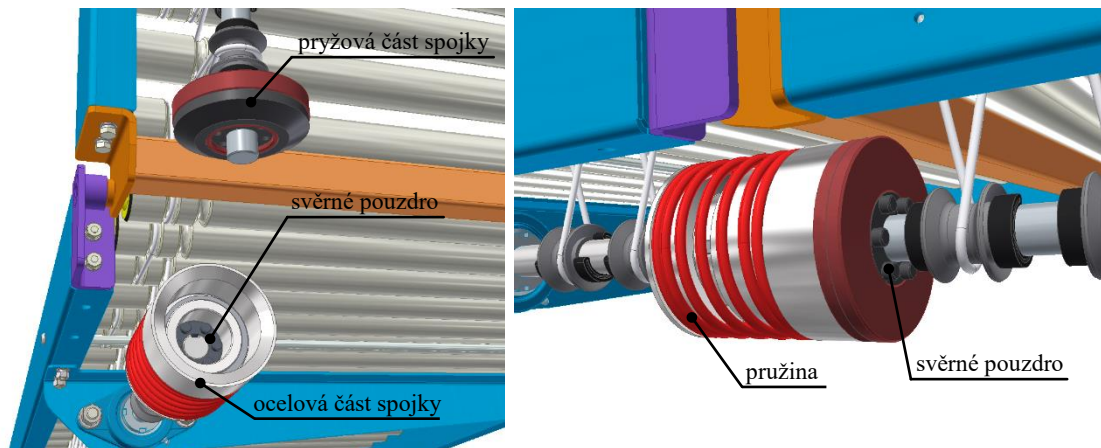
Válečkový oblouk driveshaft: a) součást linky, b) detailní pohled na konstrukční prvky. [3]
